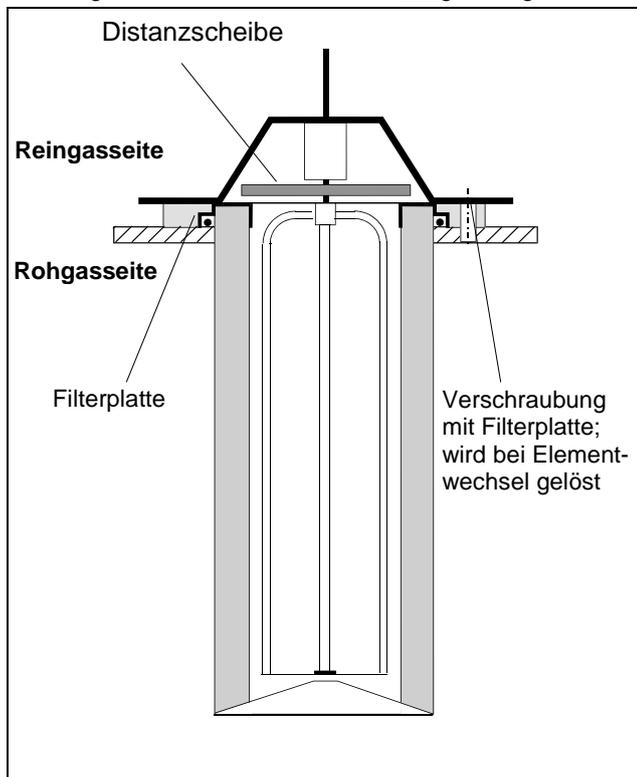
Rotationsluftdüse reingasseitige Ausführung
